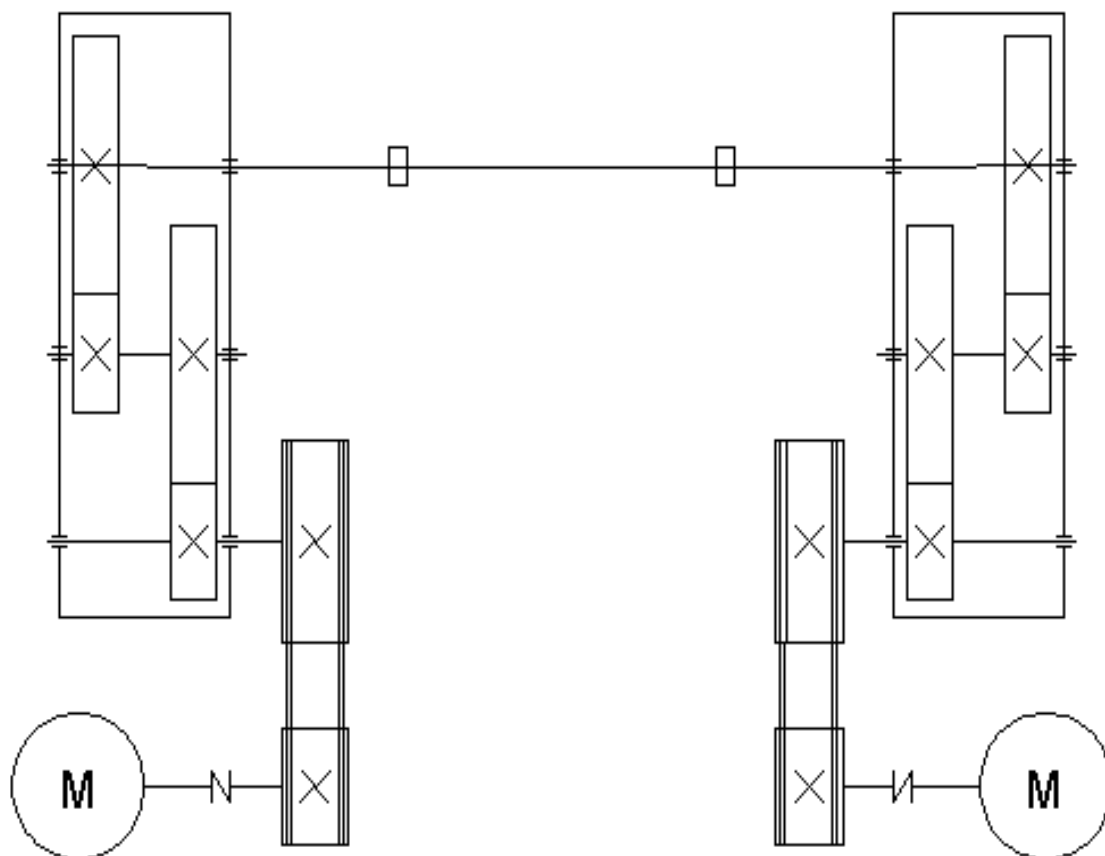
Кинематическая схема привода черпаковой цепи
